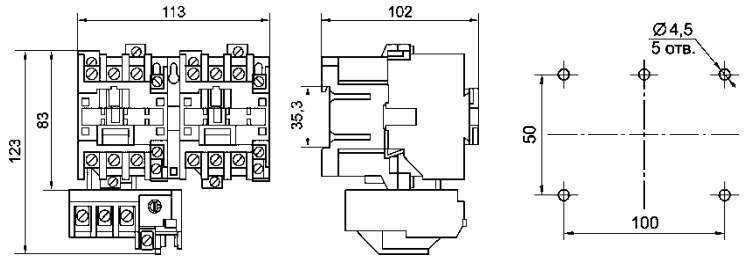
Пускатель реверсивный ПМ12-025 25А.
